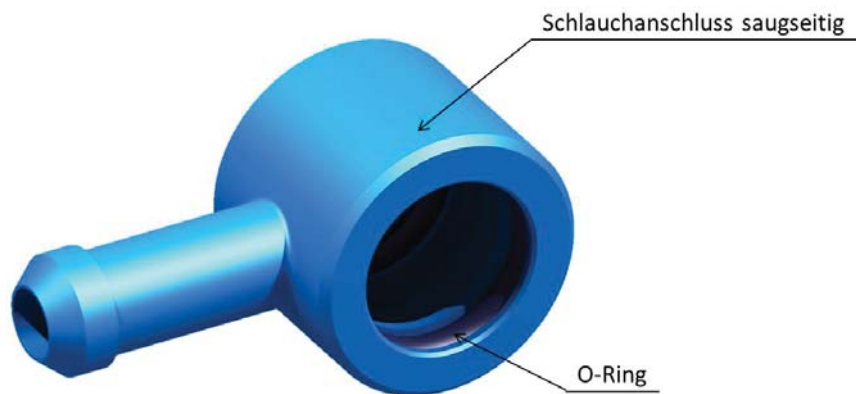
Saugseitiger Schlauchanschluss und O-Ringe
